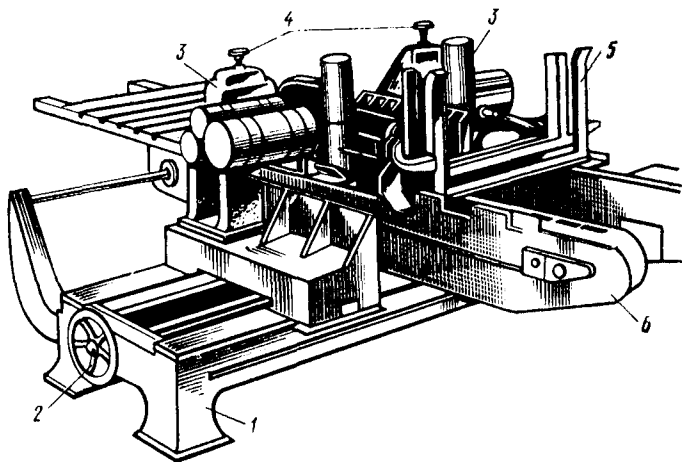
Двухпильный концеварвнитель Ц2К12Ф-1:
